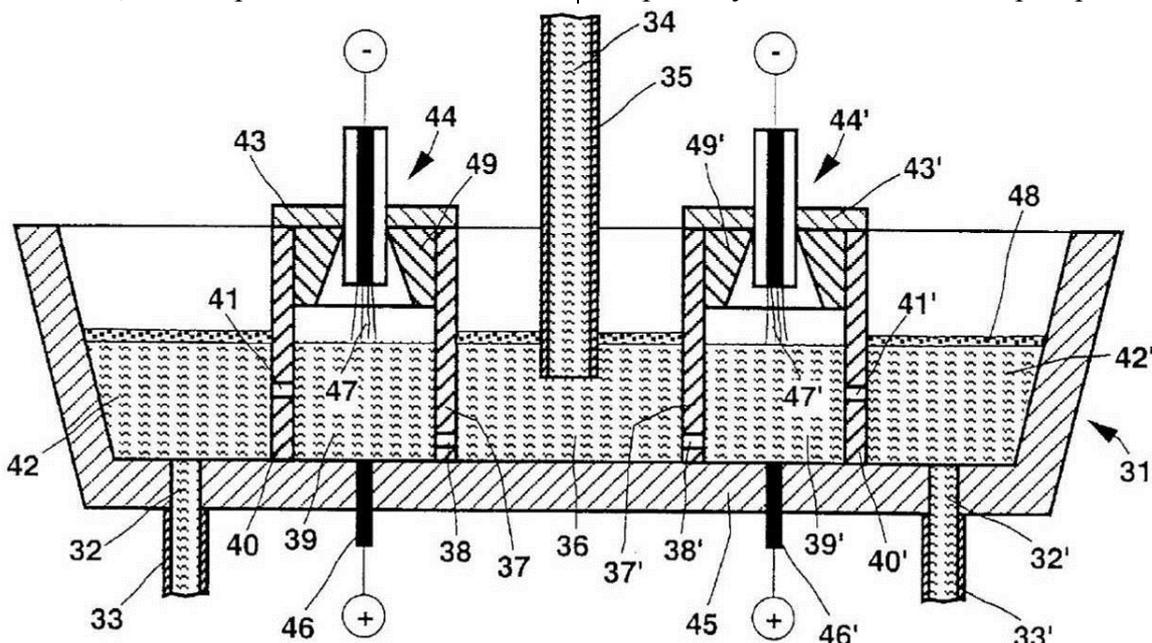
Конструкция промежуточного ковша с камерами подогрева
